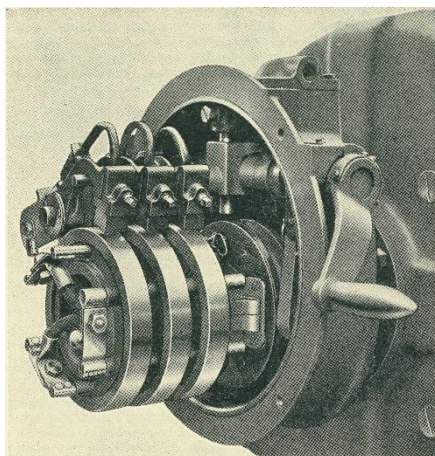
Escovas e anéis coletores de um motor de indução com rotor bobinado [3]
